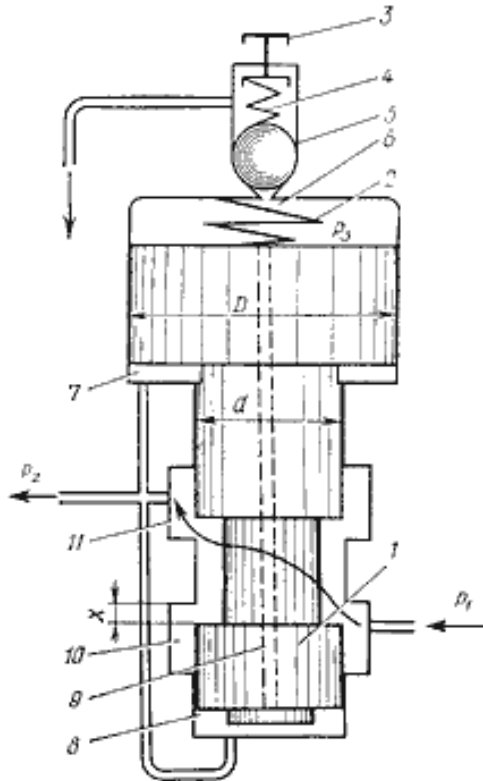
Принципова схема редуційного клапана непрямої дії
